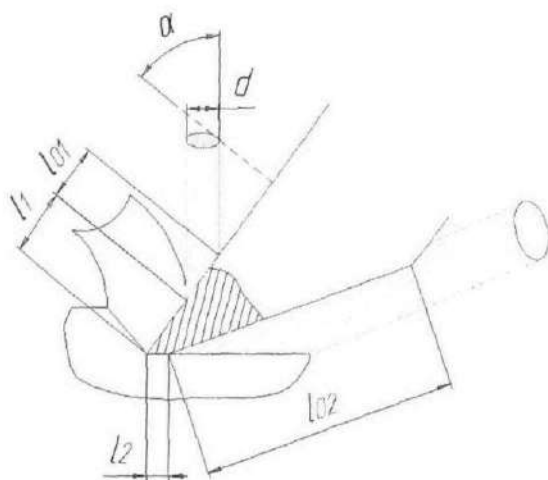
Схема охлаждения режущего инструмента при подаче СОТС передней и задней поверхностью режущего клина.
